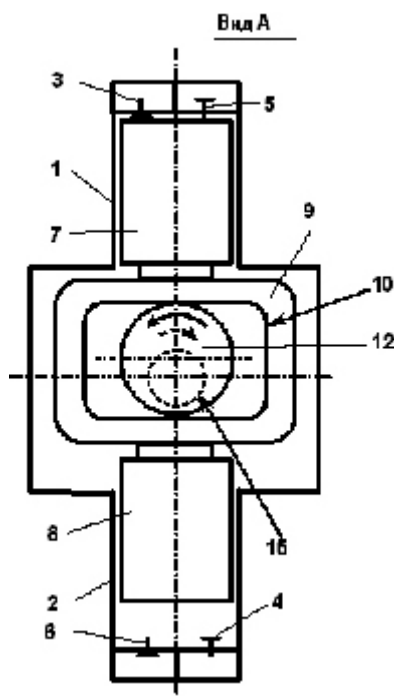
Схема поперечного сечения конструкции оппозитного компрессора с совмещенными электродвигателями (положение блока поршней «посередине»)
